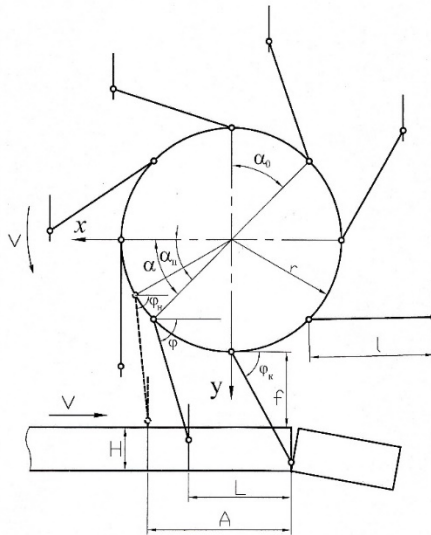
Кинематическая схема роторного устройства с плоскими ножами для резки мыла
